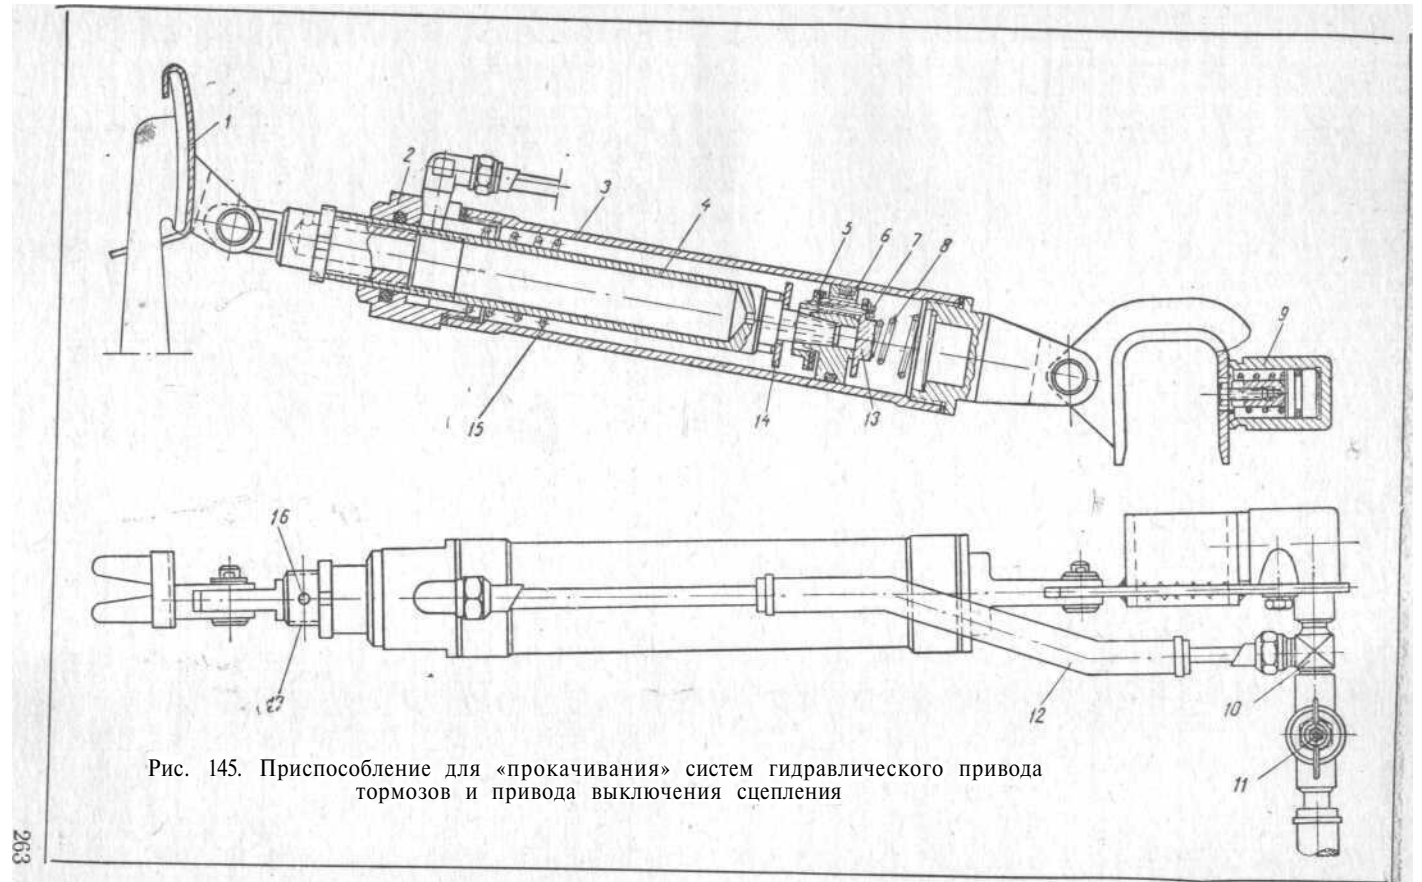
Приспособление для «прокачивания» систем гидравлического привода тормозов и привода выключения сцепления
